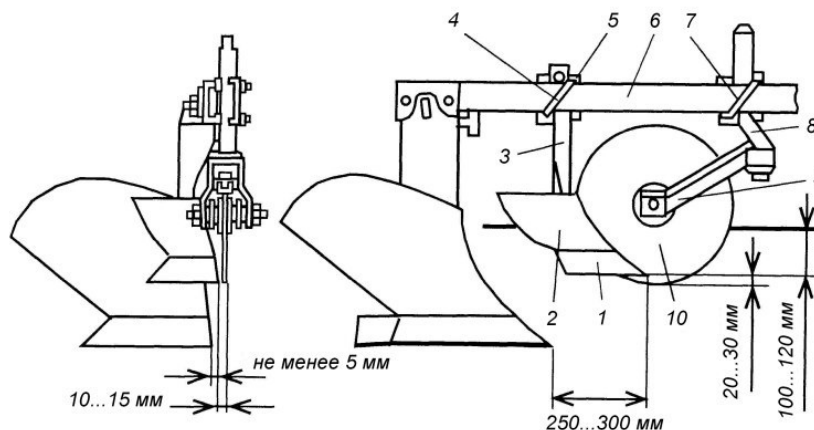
Настройка плуга: 1 – лемех; 2 – отвал; 3 – стойка; 4 и 7 – скобы; 5 – державка; 6 – грядиль; 8 – коленчатая стойка; 9 – вилка; 10 – дисковый нож
